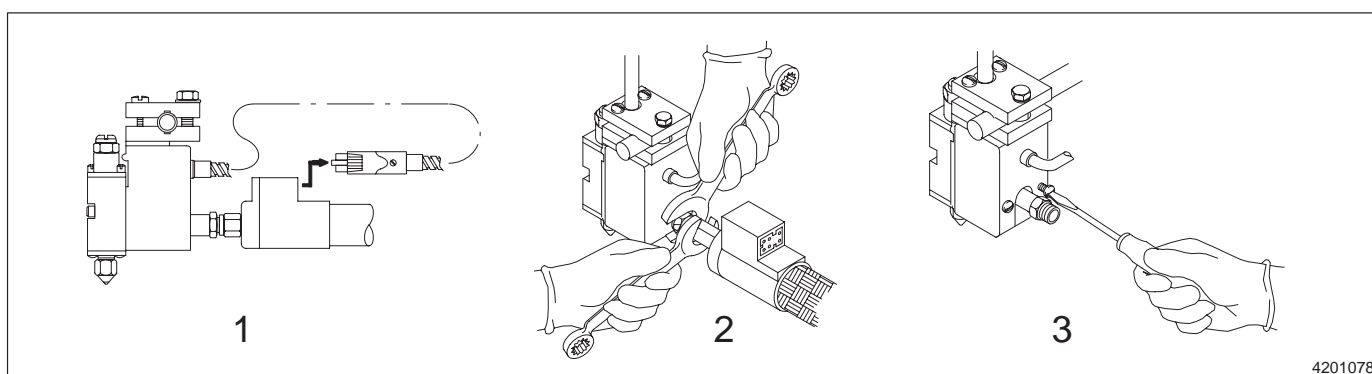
Déconnexion d'un pistolet en vue de sa réparation (cas type)
